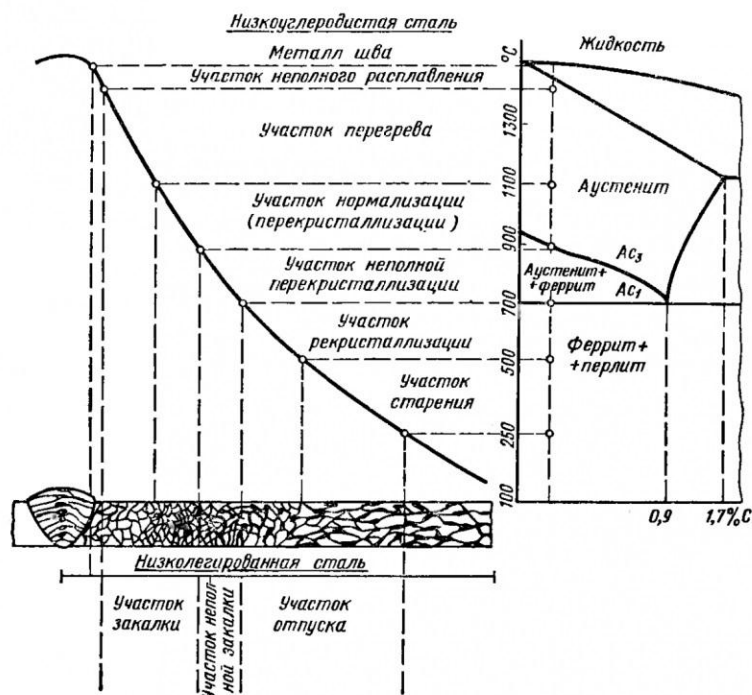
Строение сварного соединения после ручной дуговой сварки
